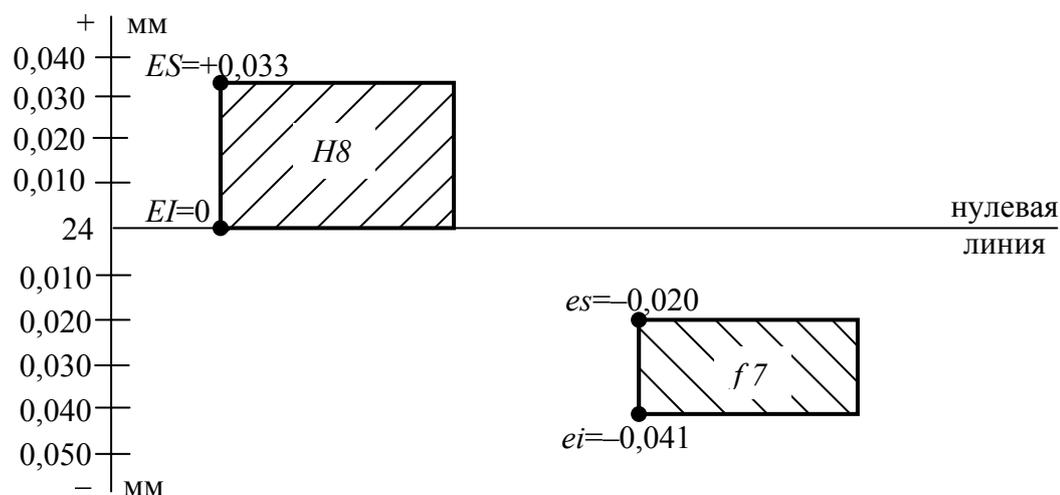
Схема расположения полей допусков деталей
